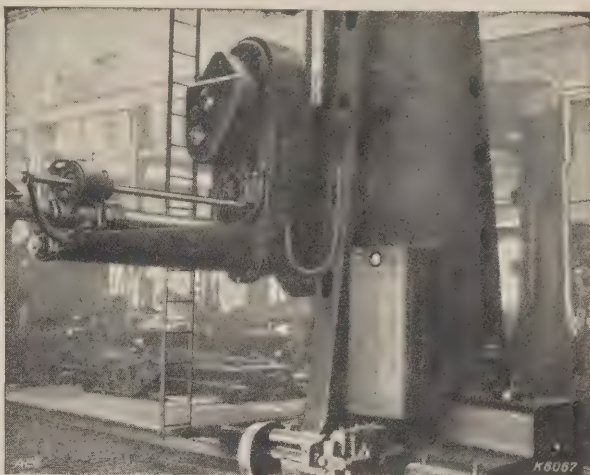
Rückansicht der Horizontal-Bohr- und Fräsmaschine (Bild 1).
